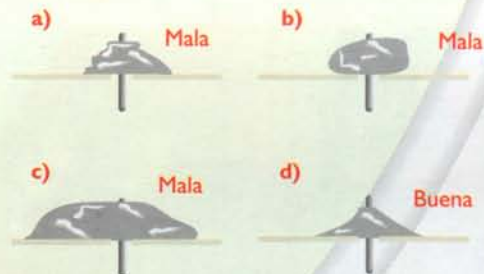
Aspecto de una buena soldadura y varias mal hechas
